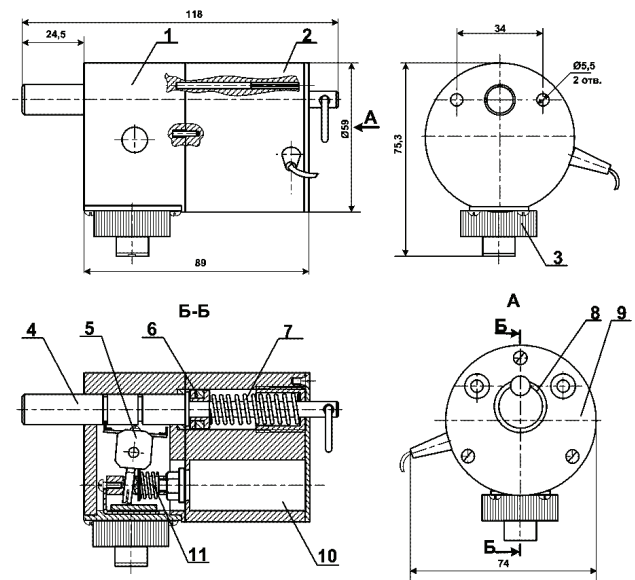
Конструкция: 1 – основание, 2 – цилиндр, 3 – устройство аварийного деблокирования, 4 – шток, 5 – механизм блокировки, 6 – магнит, 7 – пружина, 8 – кольцо, 9 – крышка, 10 – электромагнит, 11 – пружина
